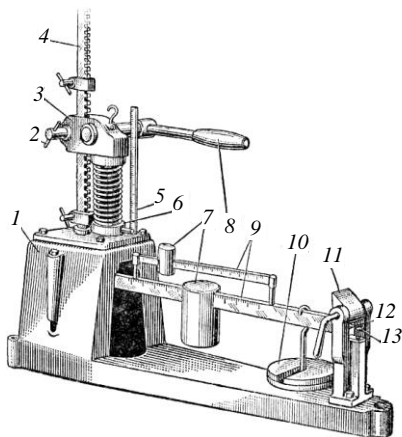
Проверка упругости пружин прибором КИ-040А: 1 – корпус; 2 – стопорный винт; 3 – передвижной кронштейн; 4 – зубчатая стойка; 5 – линейка; 6 – столик; 7 – груз; 8 – рукоятка; 9 – шкала; 10 – гиря; 11 – запорный механизм; 12 – стрелка; 13 – риска
